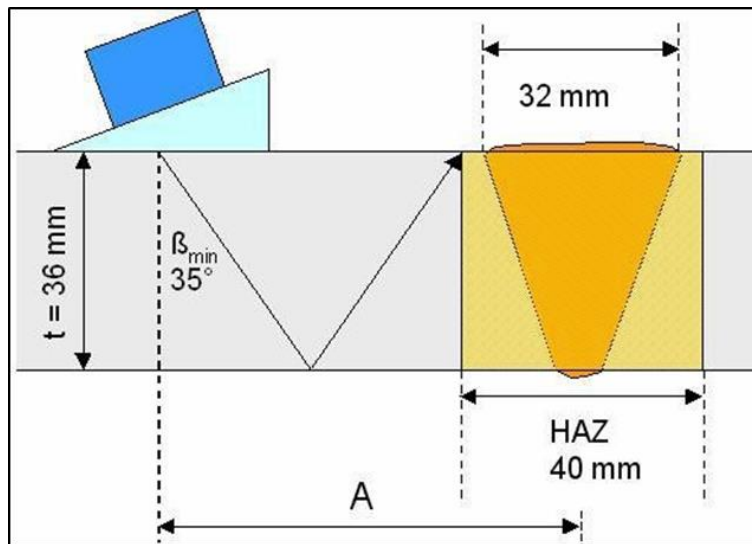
Ángulo de proyección para soldadura a tope.
